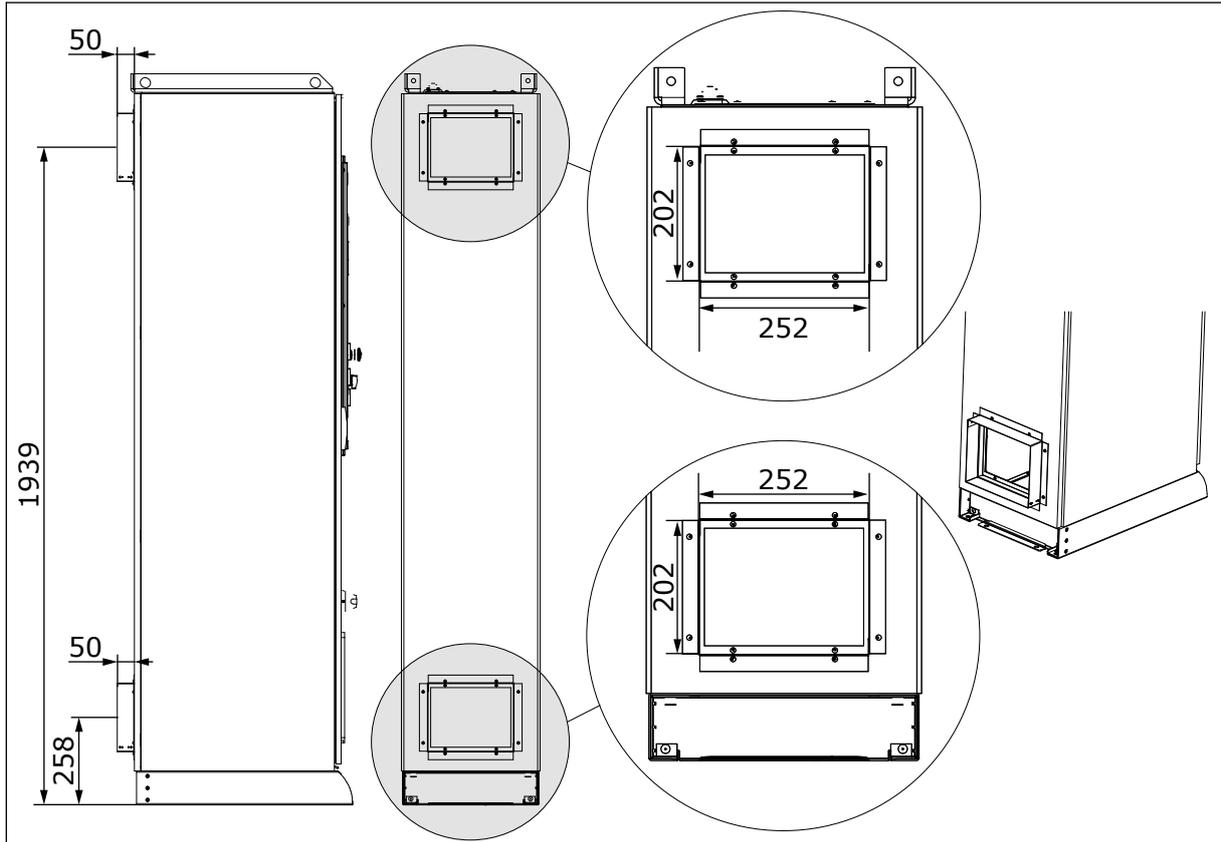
Dimensions du refroidissement par canal arrière, MR8
